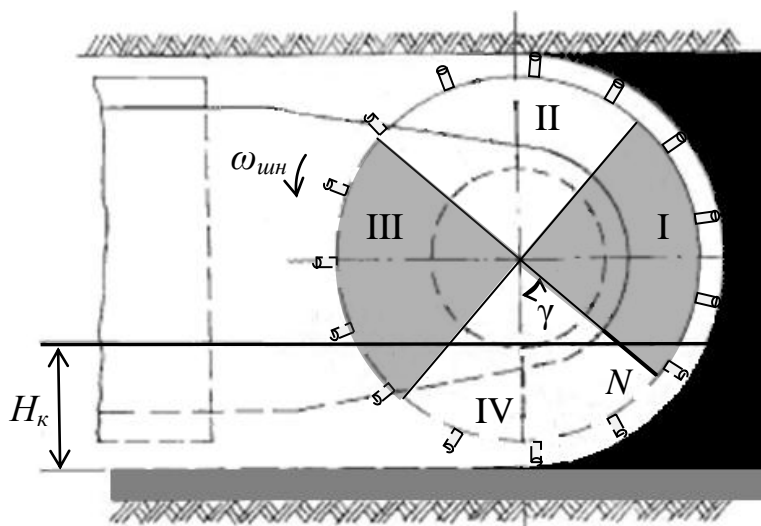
Конструктивная схема шнека (вид со стороны разгрузочного торца); линия N показывает положение конечного участка лопасти
